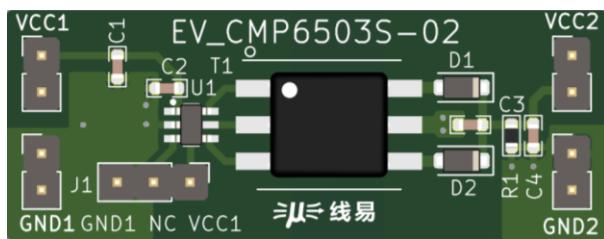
PCB 示意图(尺寸: 16 x 42mm)
